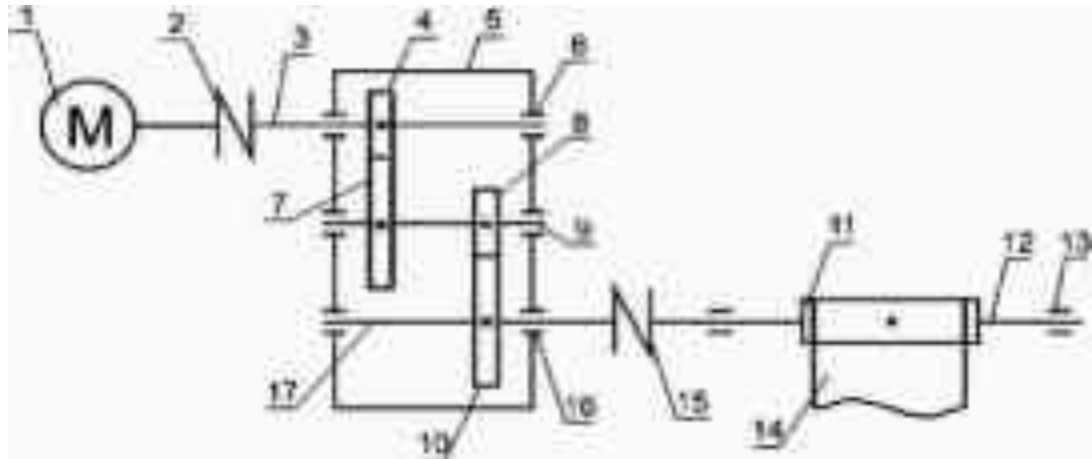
Типовий варіант привода стрічкового конвеєра: 1 – електродвигун; 2,15 – муфти (МУВП); 3 – швидкохідний (привідний) вал; 4,7 – 1-ий зубчастий ступінь; 5 – корпус; 6,9,16 – підшипникові вузли; 8,10 – другий зубчастий ступінь; 11 – привідний барабан; 12 – вал; 13 – підшипниковий вузол; 14 – конвеєрна стрічка; 17 – тихохідний (відомий) вал
